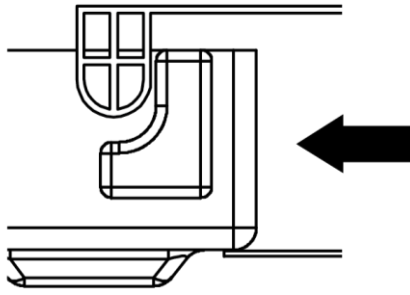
Detalle sistema tope para extracción parcial de la bandeja.
